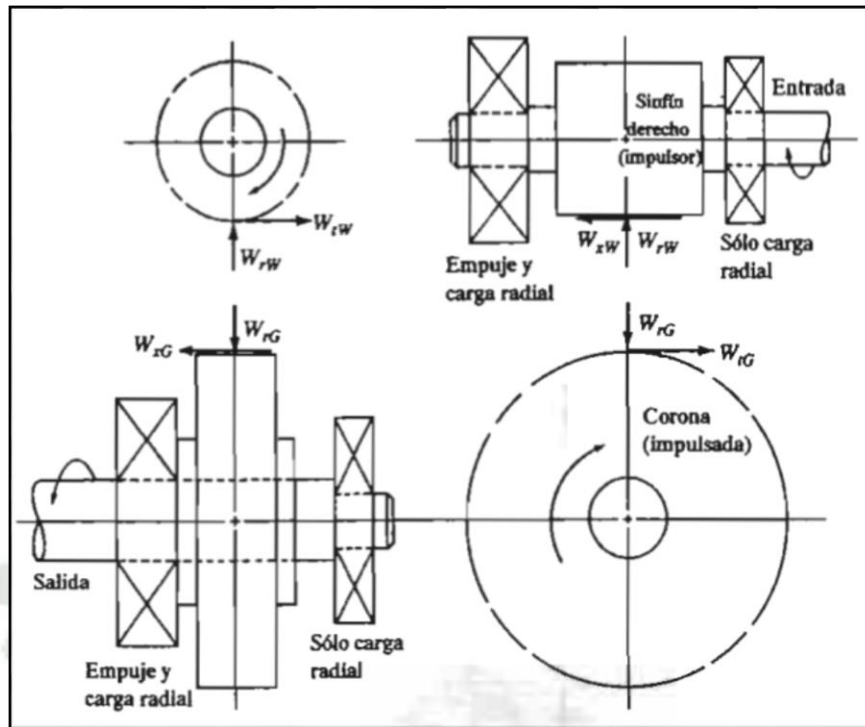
Fuerzas sobre tornillo sinfín y rueda dentada.
